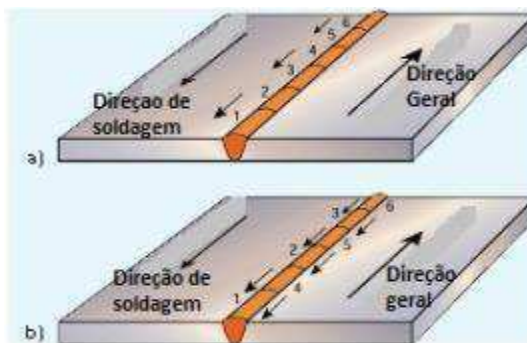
Sequencias de soldagem que minimizam as distorções, a) passe ré, b) interpasse. (TWI,2014).
